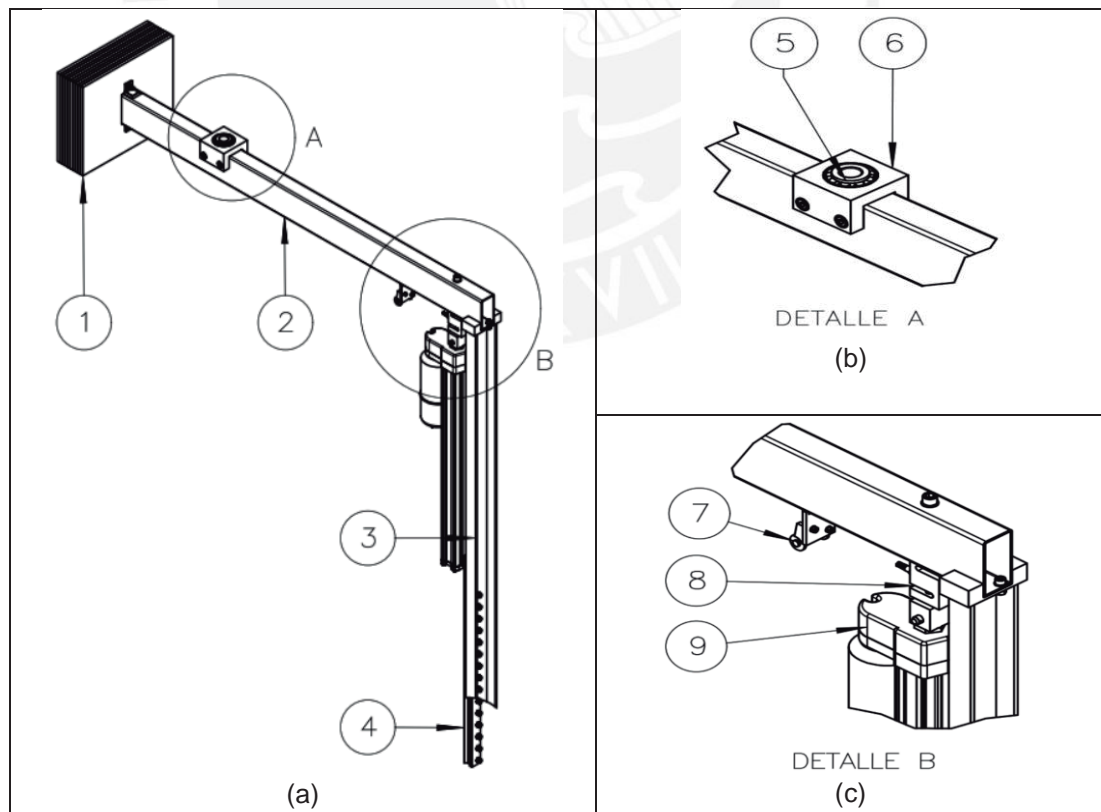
Sub-ensamble viga-columna central. a) Vista isométrica. b) Detalle A del mecanismo. c) Detalle B del mecanismo. Fuente: Propia
